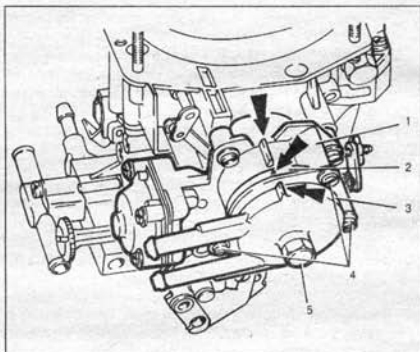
Проверка установки биметаллической пружины полуавтоматического пускового устройства карбюратора:
